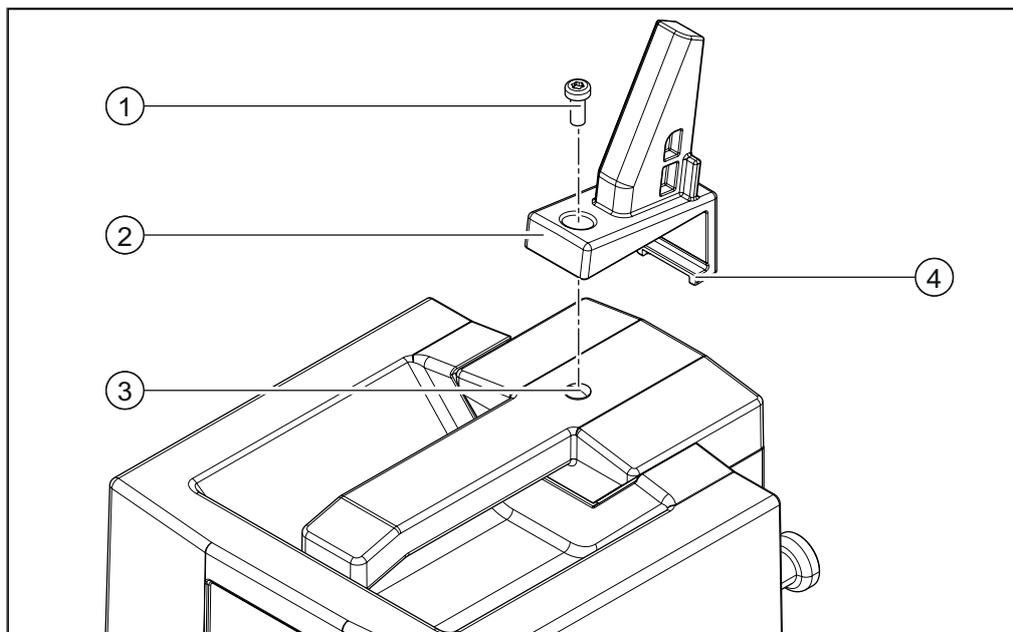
Montagem do dispositivo de fixação para a Interface I-100
